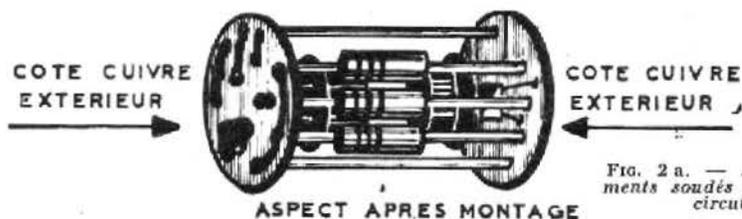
a. — Disposition des éléments soudés aux deux disques à circuit imprimé
